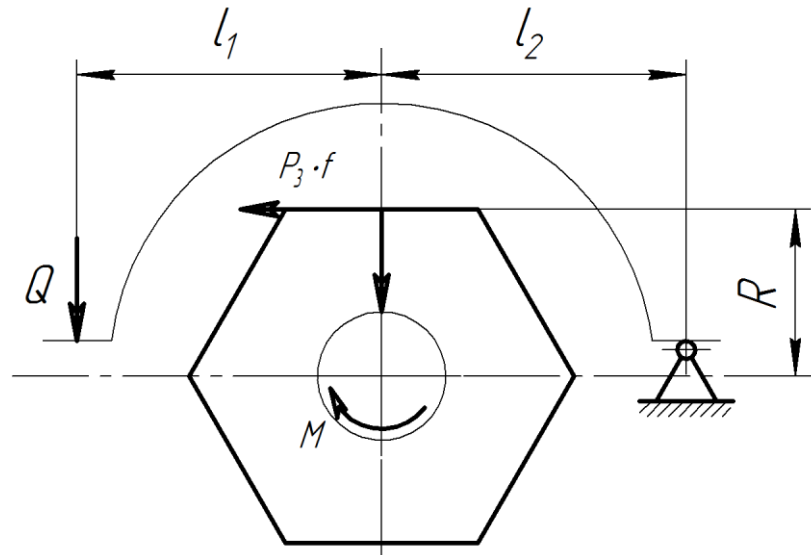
Схема розташування зусилля на осі гвинта.
